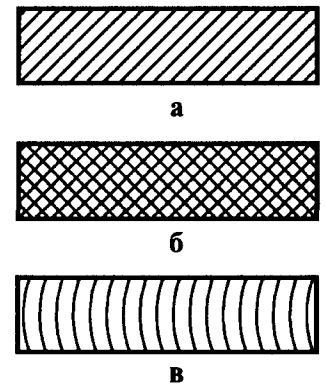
Виды штриховки деталей в сечениях и разрезах: а – металлы и твердые сплавы; б – неметаллические материалы; в – древесина
